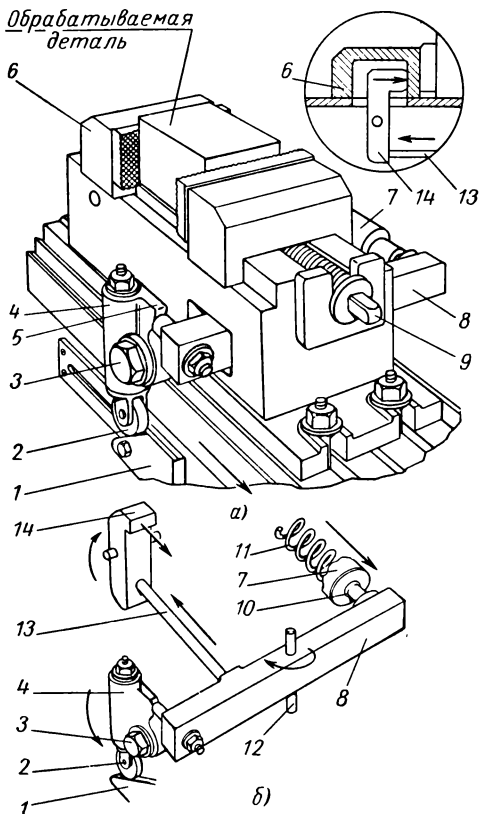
Автоматизированные тиски с головкой, смонтированной в корпусе тисков (конструкции А. Н. Лебедева):
